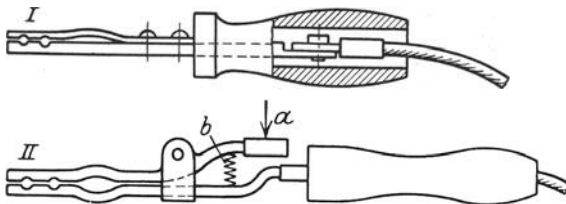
Schweißzangen für Kaltschweißungen.
